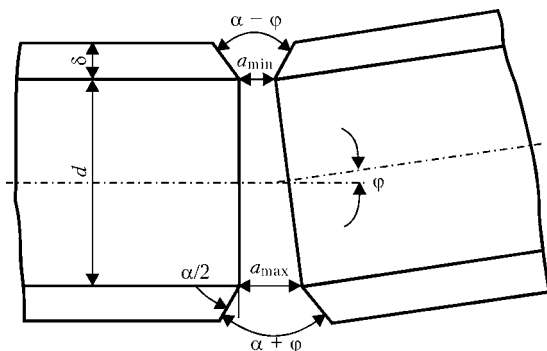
Схема сборки под сварку кольцевого стыка обечайки
